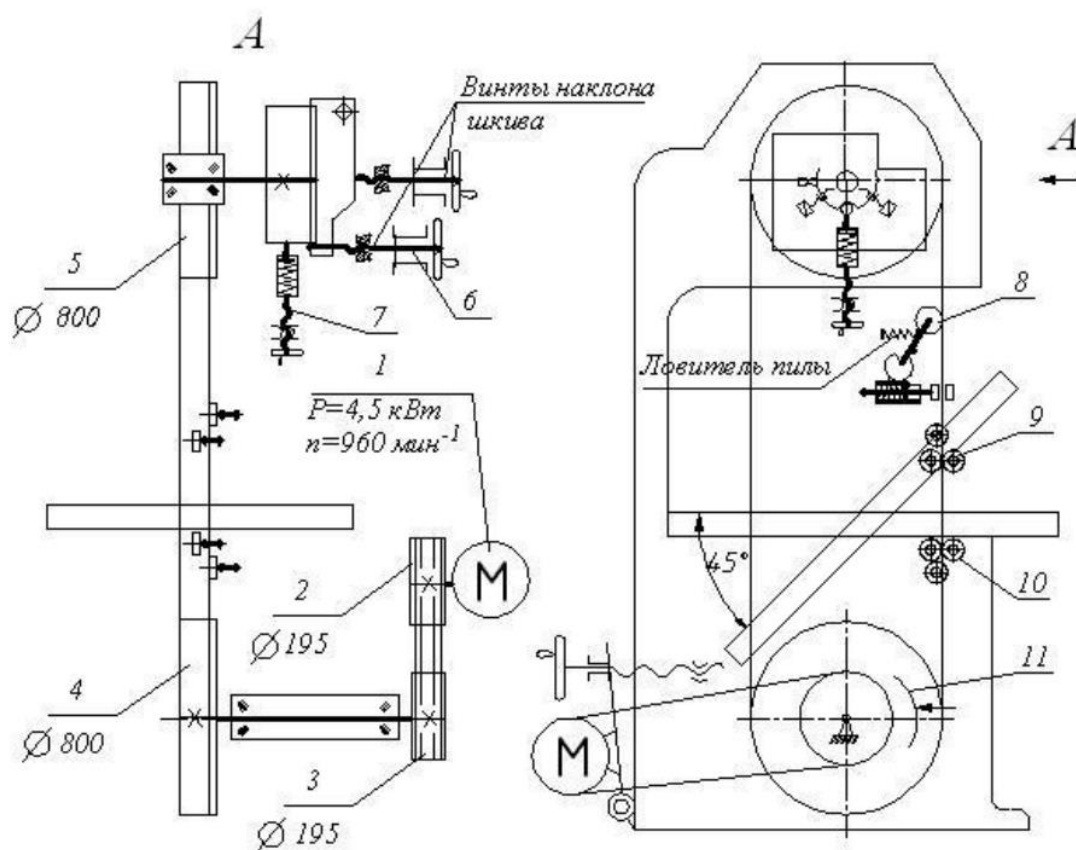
Кинематическая схема ленточнопильного станка ЛС-80-5
